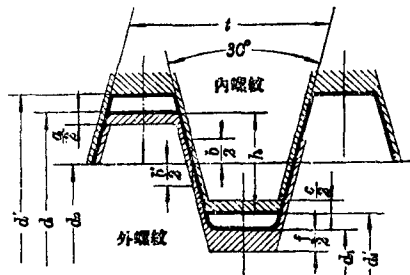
1 级精度梯形螺纹公差带位置的配置
